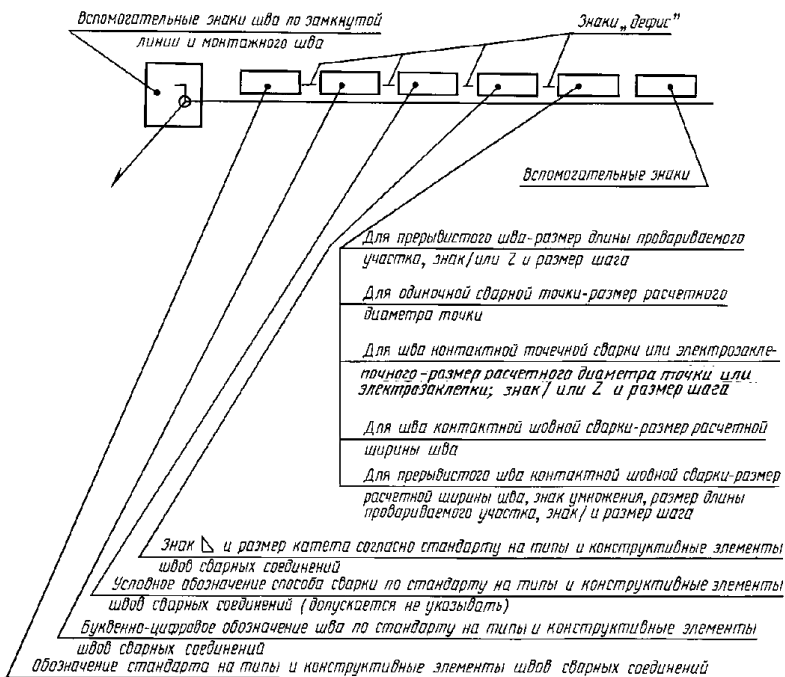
Структура условного обозначения шва сварного соединения
